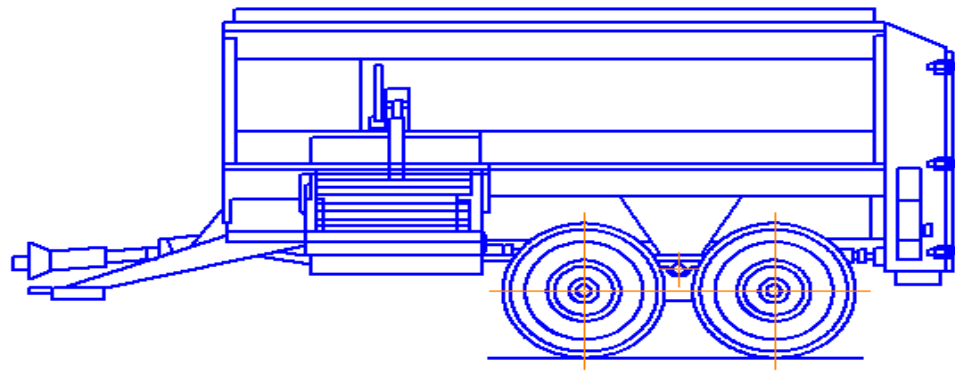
Модернизированный смеситель-кормораздатчик РСП-10
